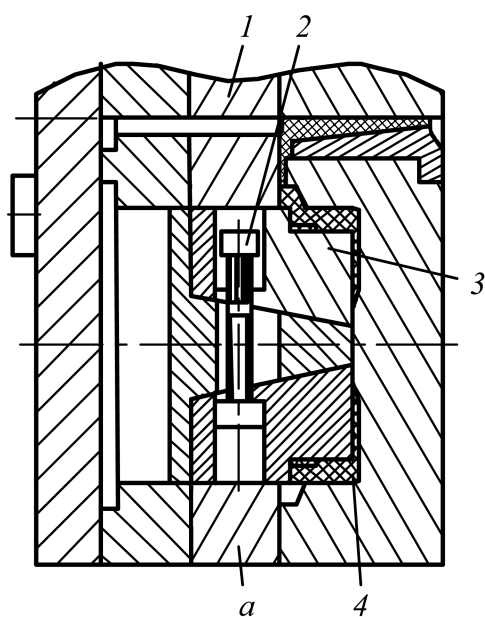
Форма для оформления резьбы на внутренней поверхности изделия с клиновыми резьбовыми знаками
